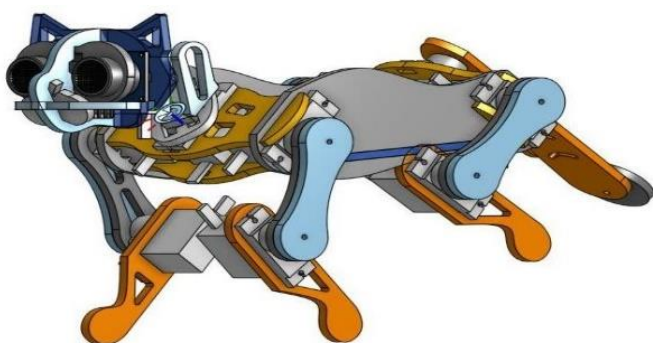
Molde do corpo (<https://cad.onshape.com>).
